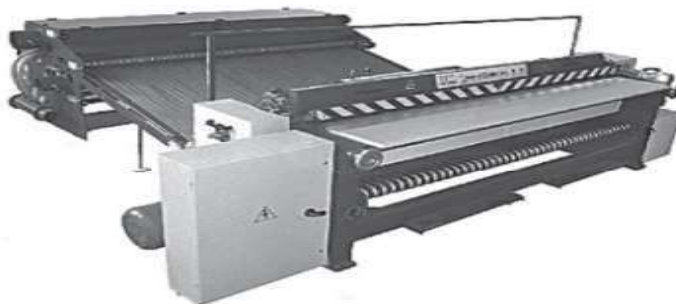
Агрегат для полировки и обеспыливания готовой продукции модели GMSG2, производства компании Young-Pearl Machinery Co., Ltd (Китай)
